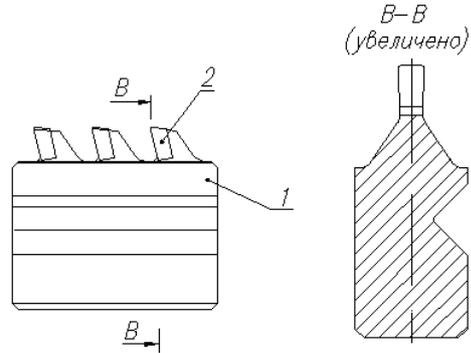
Экспериментальные трехзубые протяжки с напайными твердосплавными пластинами
